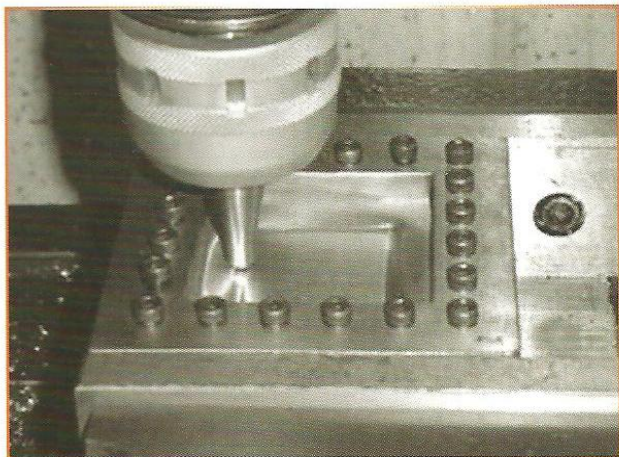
Estampagem incremental de uma chapa por uma máquina CNC⁽⁶⁾
